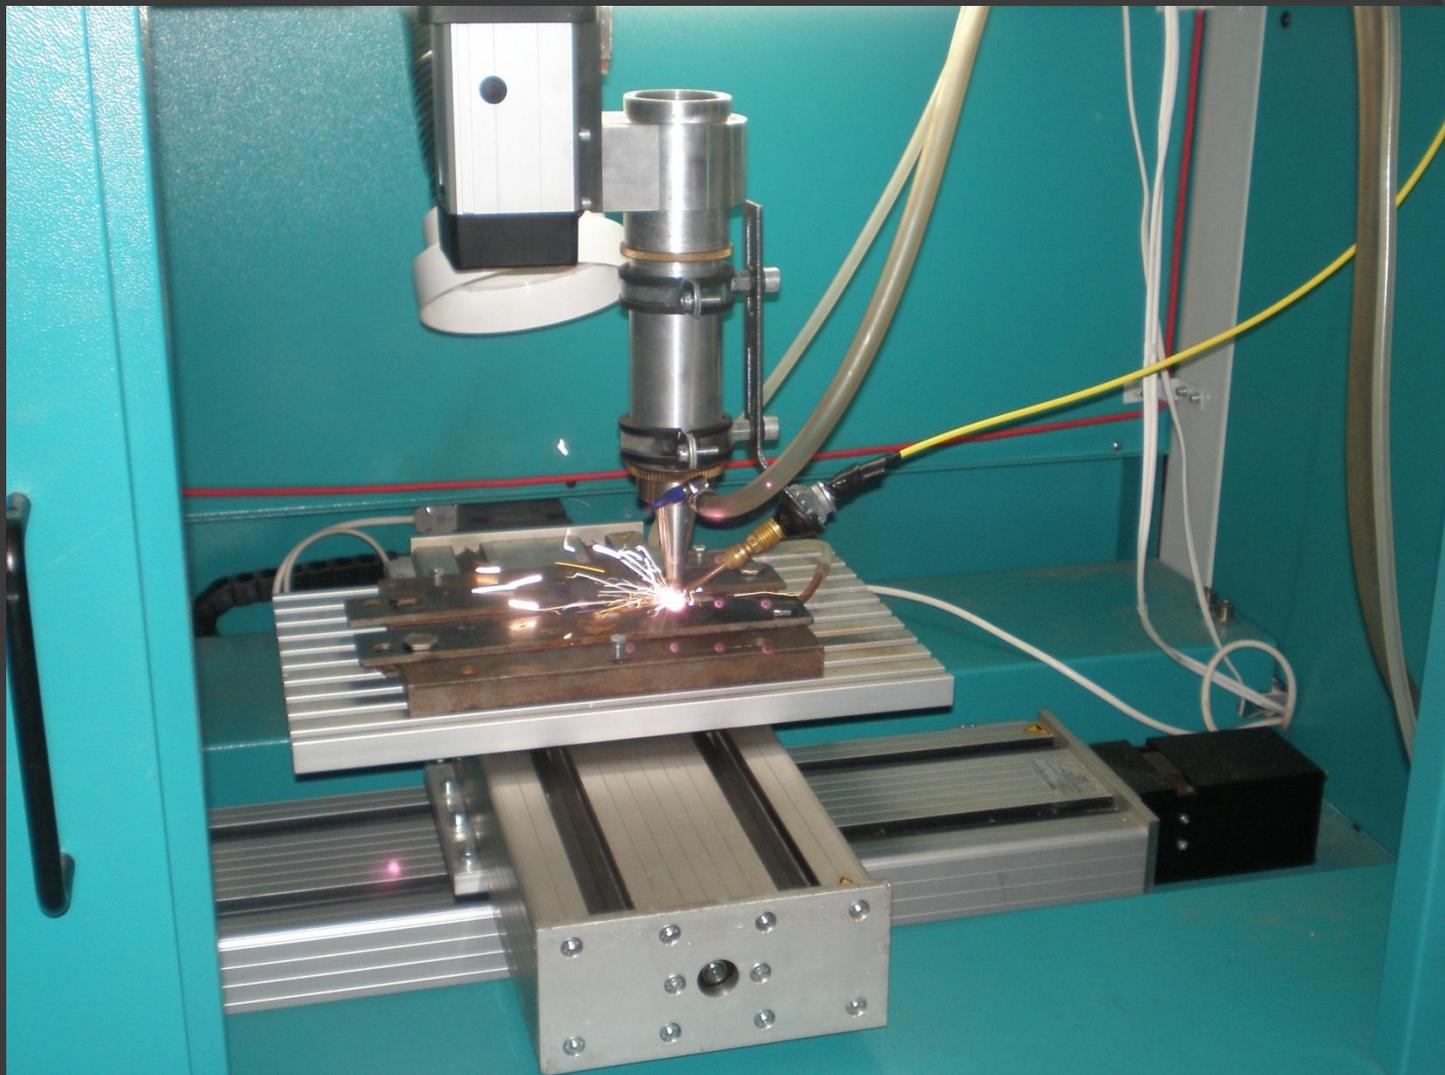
Процесс сварки с присадочной проволокой.
